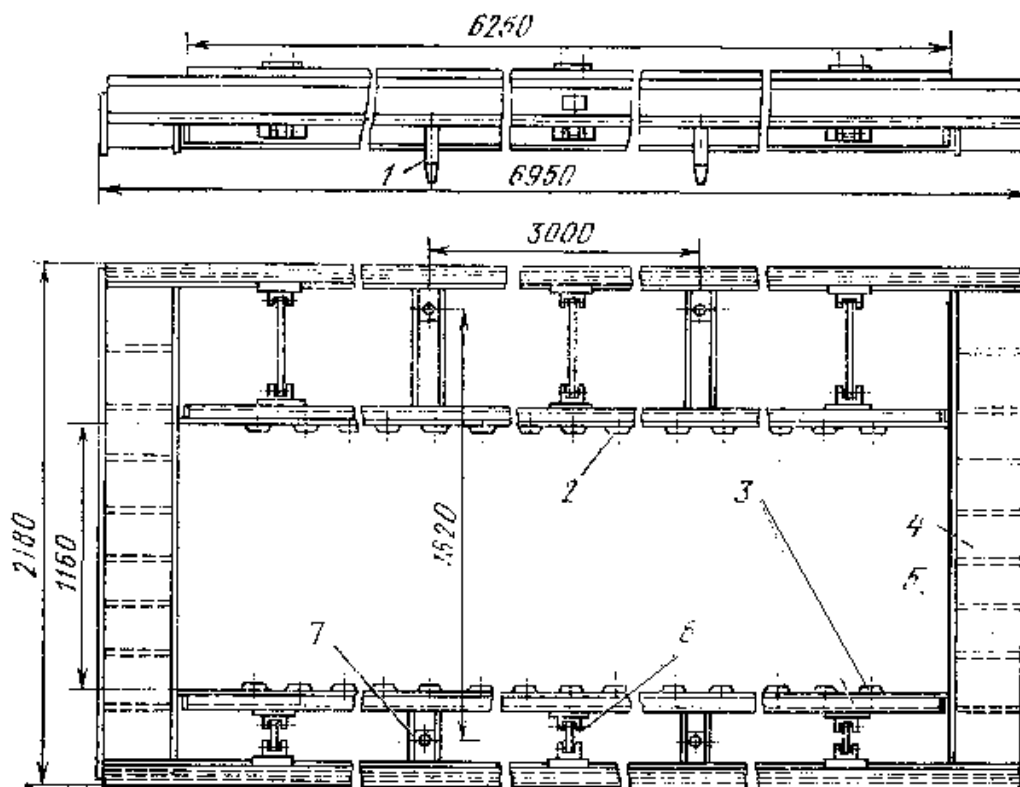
Бортоснастка СМЖ-600/1Б для изготовления многпустотных панелей перекрытий:
